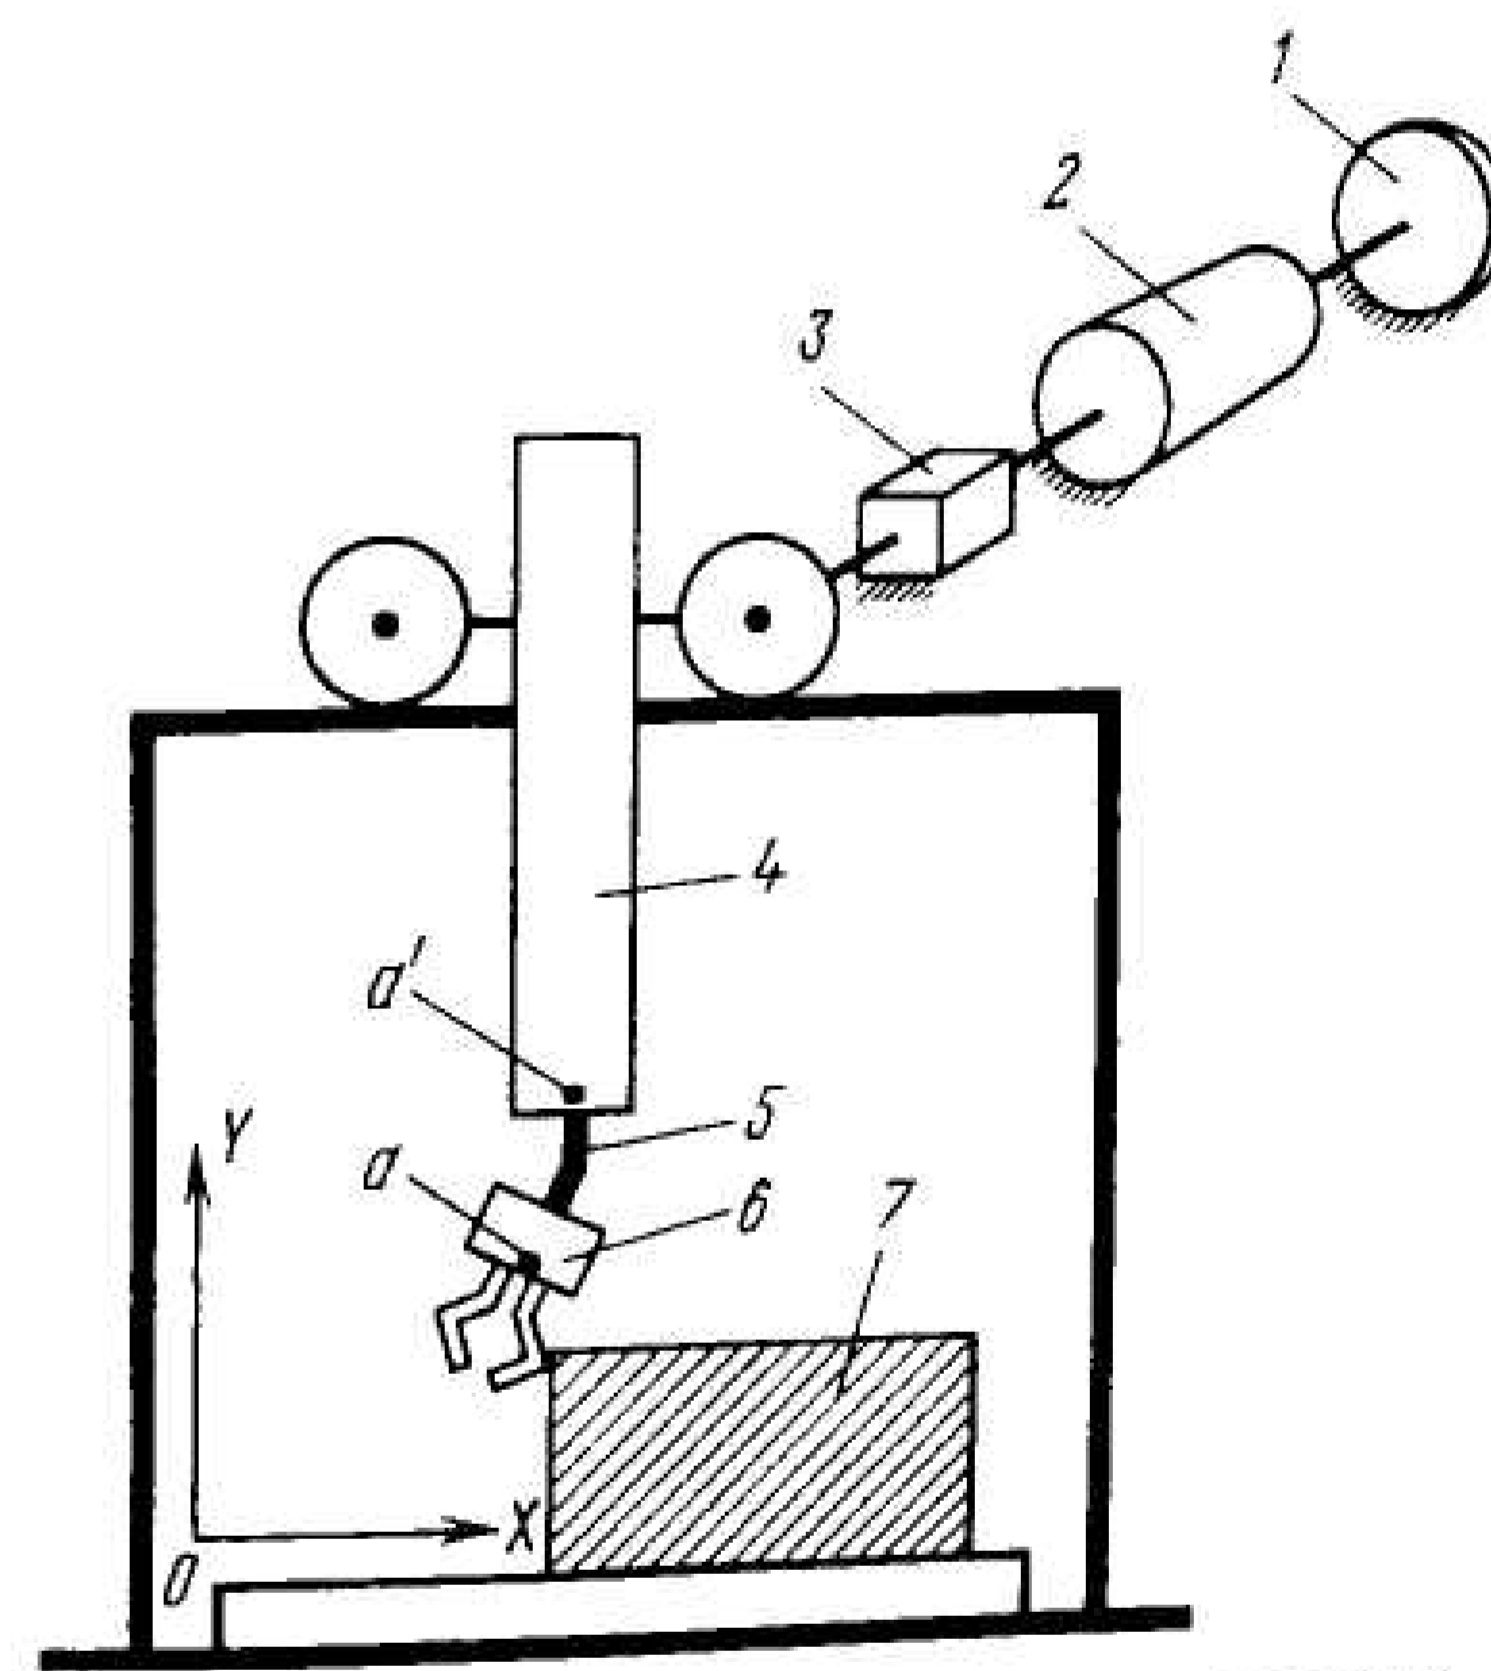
Манипулятор с упругим датчиком: 1 — тахогенератор; 2 — двигатель; 3 — редуктор; 4 — штанга манипулятора; 5 — упругий датчик сил; 6 — схват; 7 — неподвижный предмет
